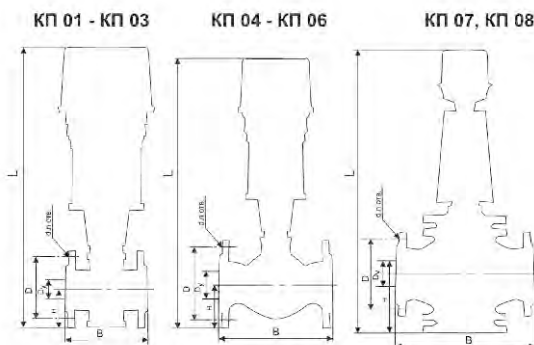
Габаритные и присоединительные размеры термомайзеров Р-8.Т.
